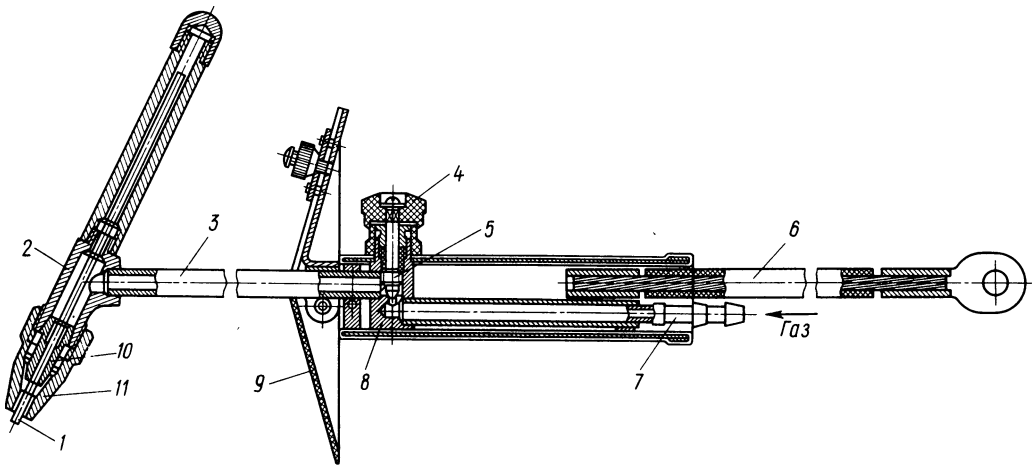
Горелка для ручной аргонодуговой сварки вольфрамовым электродом: 1 — вольфрамовый электрод, 2 — горелка, 3 — трубка, 4 — маховичок для регулирования расхода аргона, 5 — вентиль, 6 — гибкий кабель, 7 — ниппель, 8 — корпус, 9 — щиток, 10 — цапга, 11 — сопло
